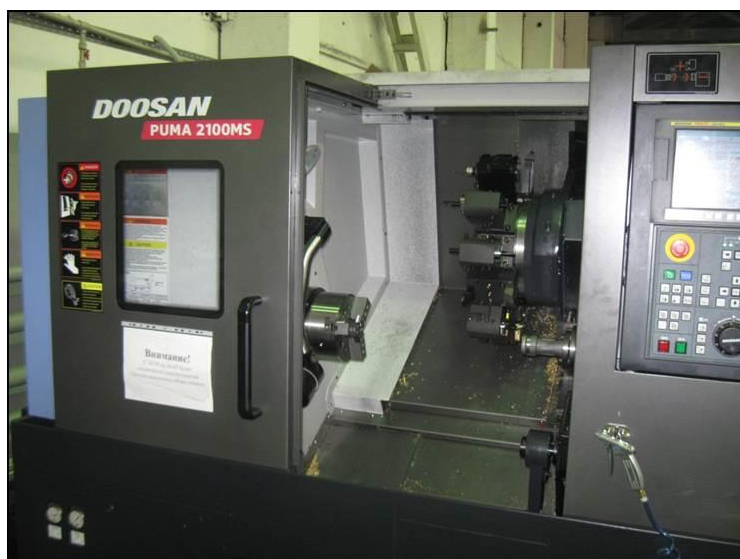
Високопродуктивний двошпindelний токарний обробний центр PUMA 2100MS із приводним фрезерним інструментом і контр-шпindelлем (“DOOSAN”)
